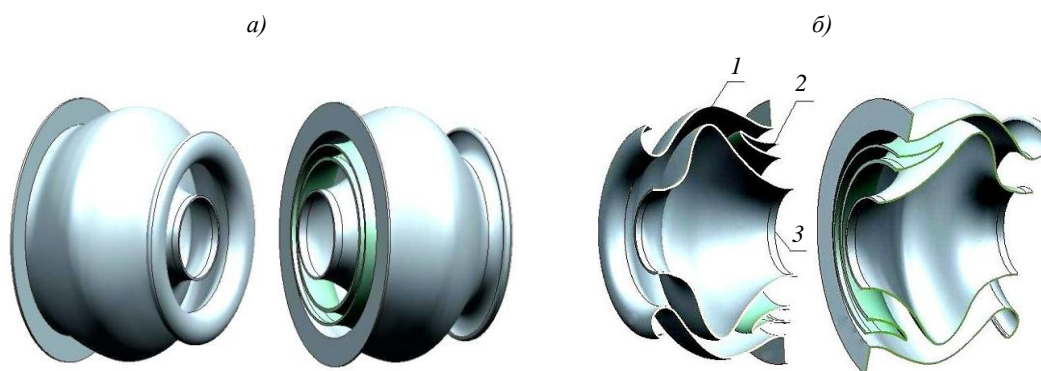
Общий вид (а) и внутренняя компоновка (б) пылезащитного устройства (без «улитки»): 1 – внешняя стенка; 2 – разделитель; 3 – внутренняя стенка
